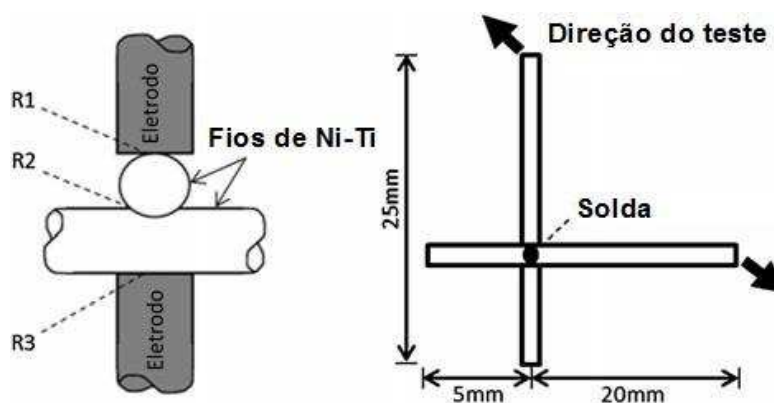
Montagem para a soldagem por resistência e esquema do teste de ruptura das juntas soldadas. Adaptado de Tam *et al.* (2012).
